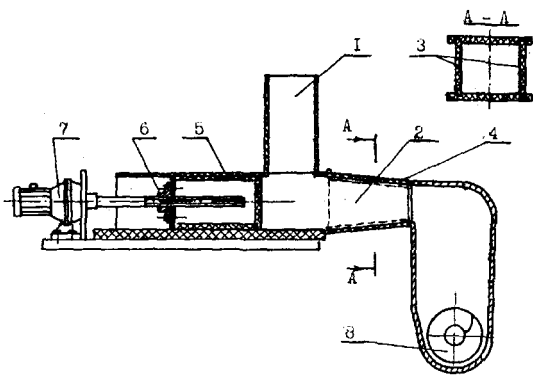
Конструктивно-технологическая схема установки с горизонтальными рабочими камерами и винтовым приводом поршней уплотнения: 1 - бункер; 2 - рабочая камера; 3 - электроды; 4 - регулируемая стенка; 5 - поршень; 6 - винтовой механизм; 7 - электропривод; 8 - выгрузной шнек.
